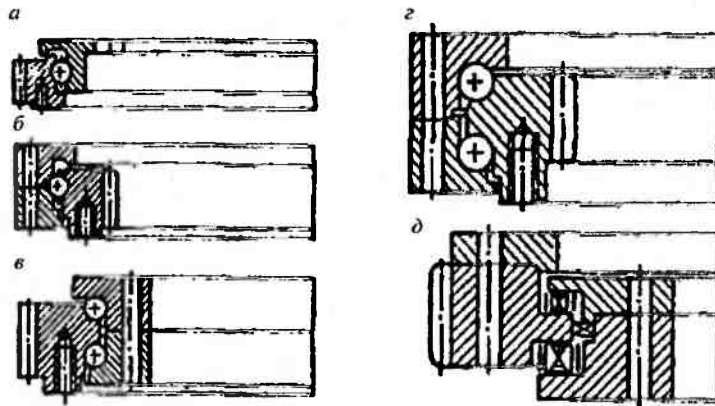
Опорно-поворотные устройства без центральных цапф с внешним и внутренним зацеплением:
